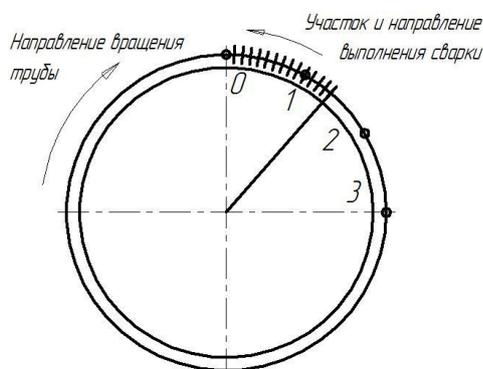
Схема выполнения сварного соединения способом МПИ с поворотом на 45°
